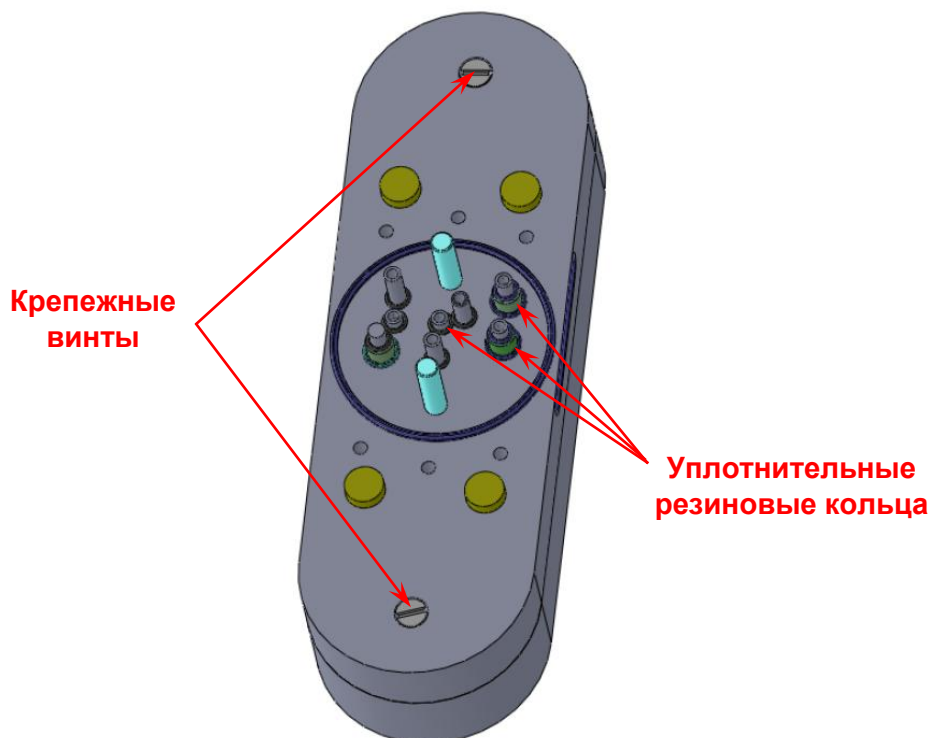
Обратная сторона ионного источника с указанием винтов крепления корпуса магнитов и мест установки уплотнительных колец.
